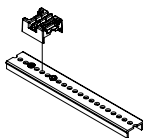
Габаритные размеры алюминиевого профиля / Figure 2 – Overall dimensions of the aluminum section / 2 сурет – Алюминий профильдің габариттік өлшемдері
